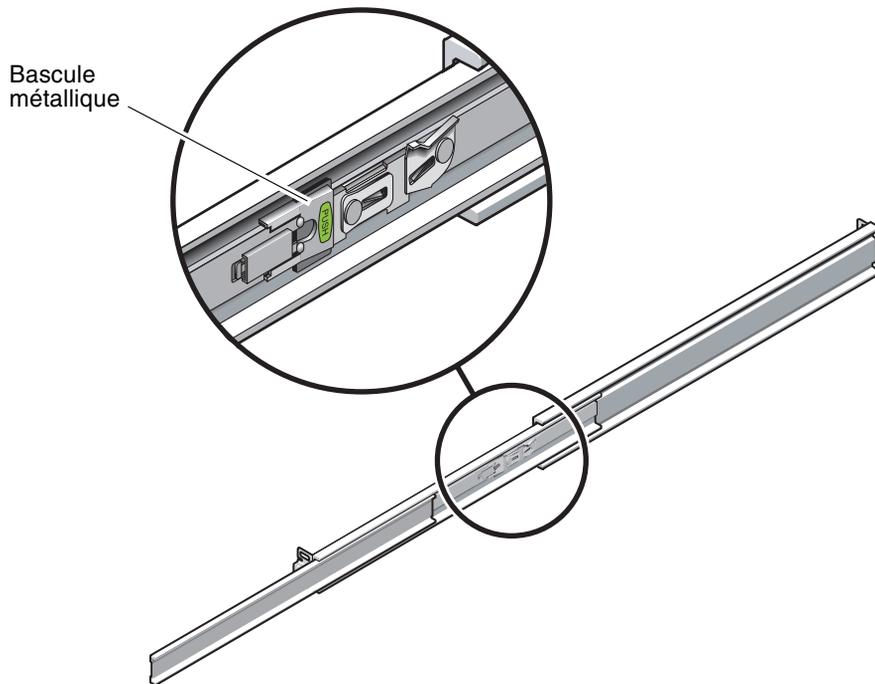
Déverrouillage de la section centrale d'un rail coulissant
